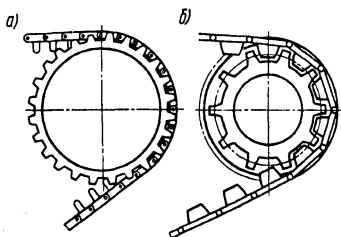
Виды зацепления ведущего колеса с гусеницей:
